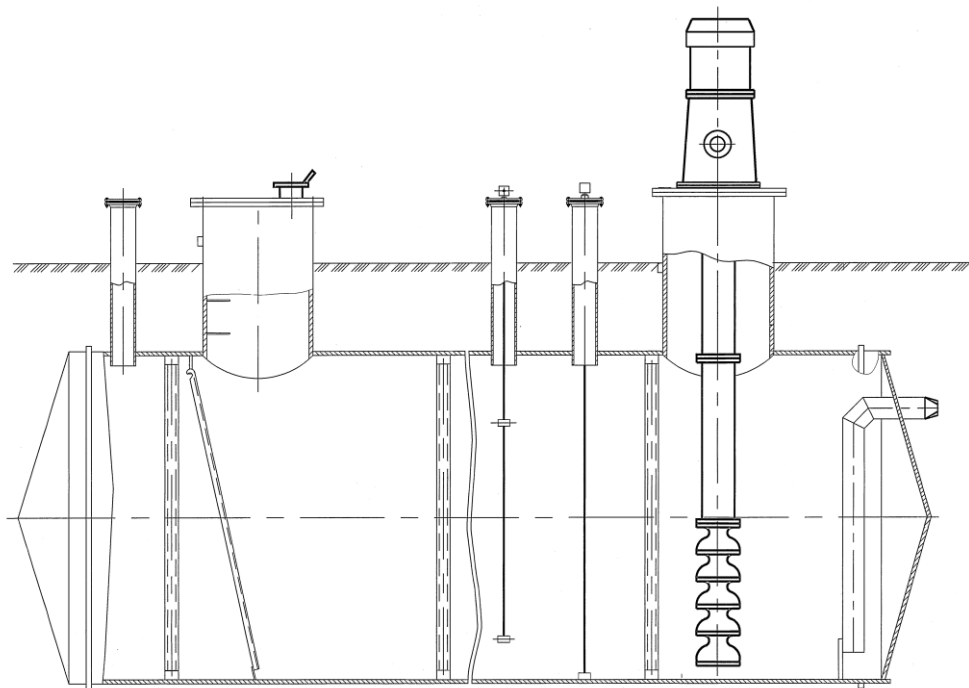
Общий вид эскиза резервуаров РГС-40 зав.№№ 76, 124, 129, 180, 181
